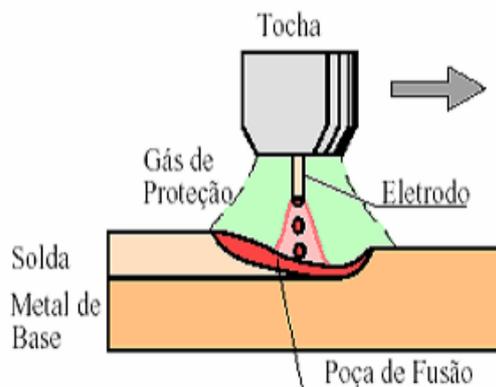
Desenho esquemático do processo de soldagem GMAW (RAMALHO e GIMENES, 2004)
